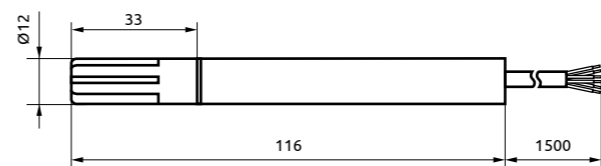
Габаритный размер НТЕ.РF с кабелем
